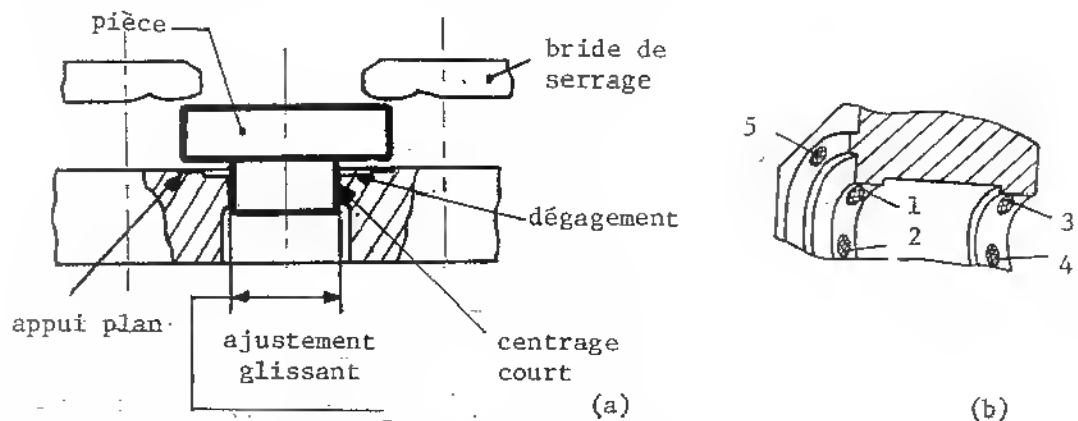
(a) Montage d'usinage avec appui plan et centrage court
